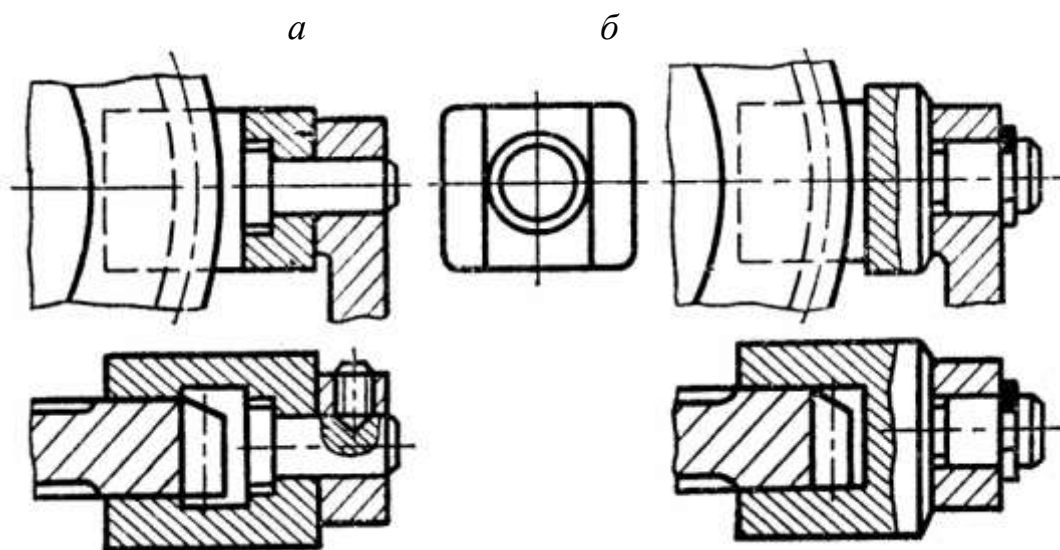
Способы крепления штифта обхватывающего сухаря (вилки) в рычаге:
